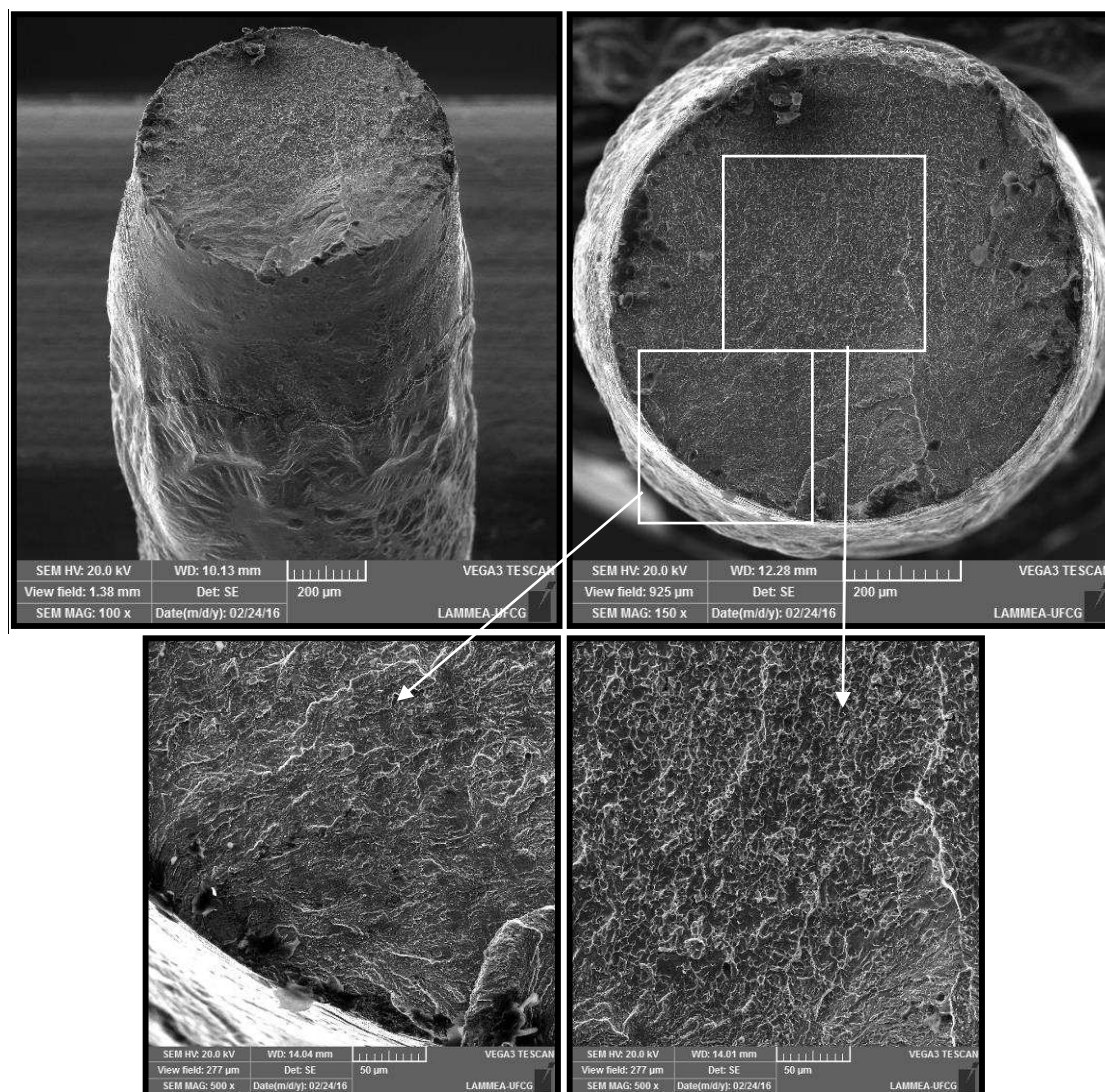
Superfície de fratura do fio superelástico soldado na configuração 8ms/65% e testado a 40°C.
